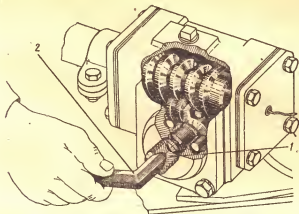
Регулировка зацепления ролика с червяком автомобиля УАЗ-69:
